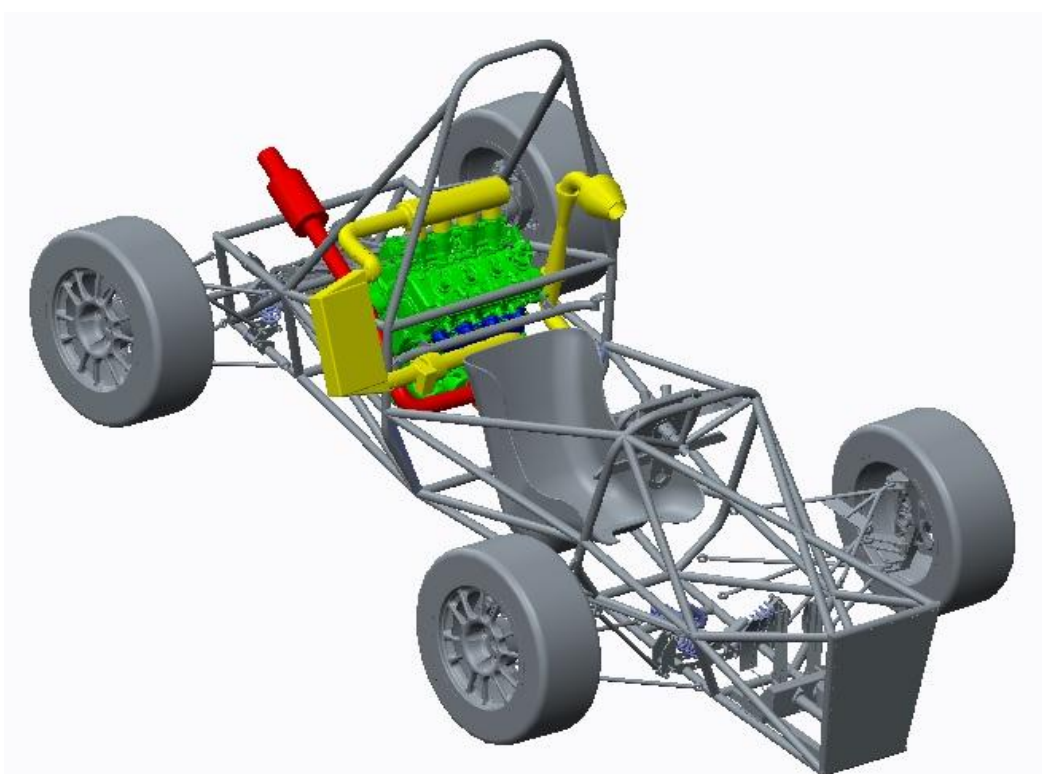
Model sestavy motoru GSX-R600 s přeplňováním.
